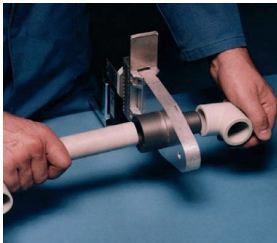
Manuelles Stumpfschweißen
